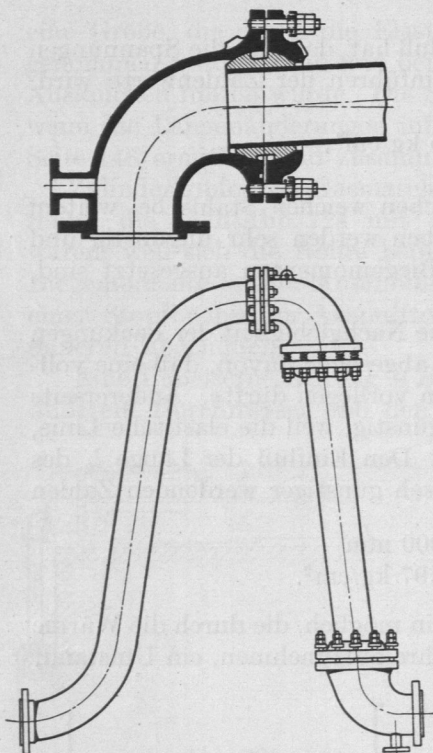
und 730. Ausgleichsvorrichtungen mit Kugelgelenken.
